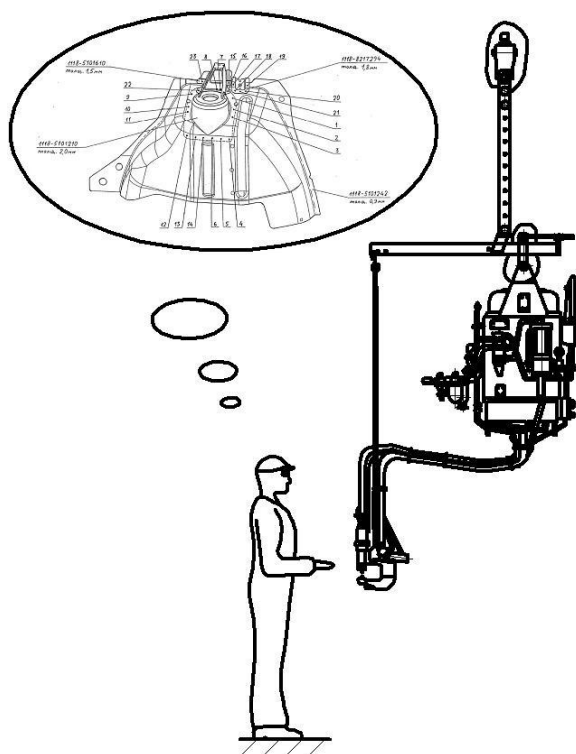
Операция сборки и точечной сварки
